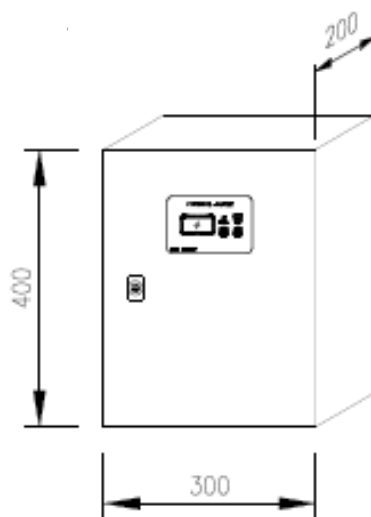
; Reaktordimensjoner (mm) for UV 80/3 Rack EPW
